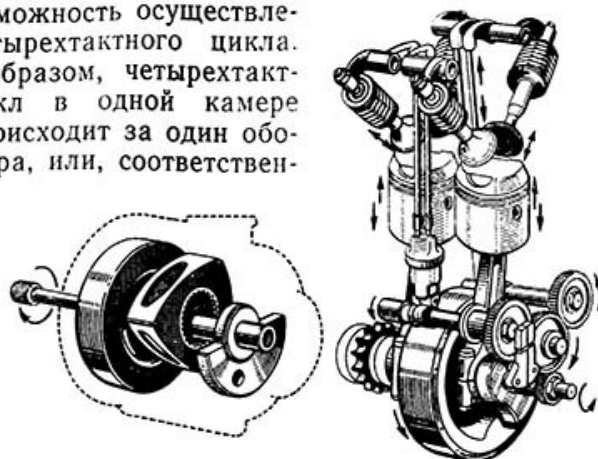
Движущиеся детали РПД и четырехтактного двухцилиндрового поршневого двигателя
